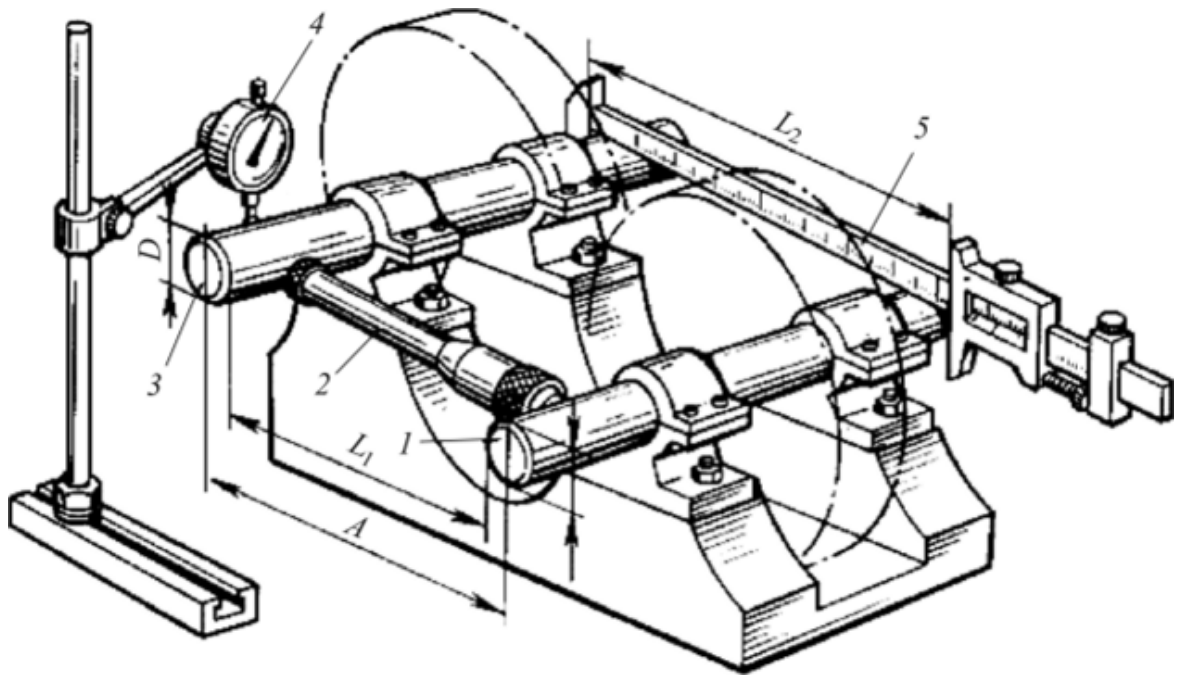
Схема контролю положення осей отворів у корпусі редуктора
